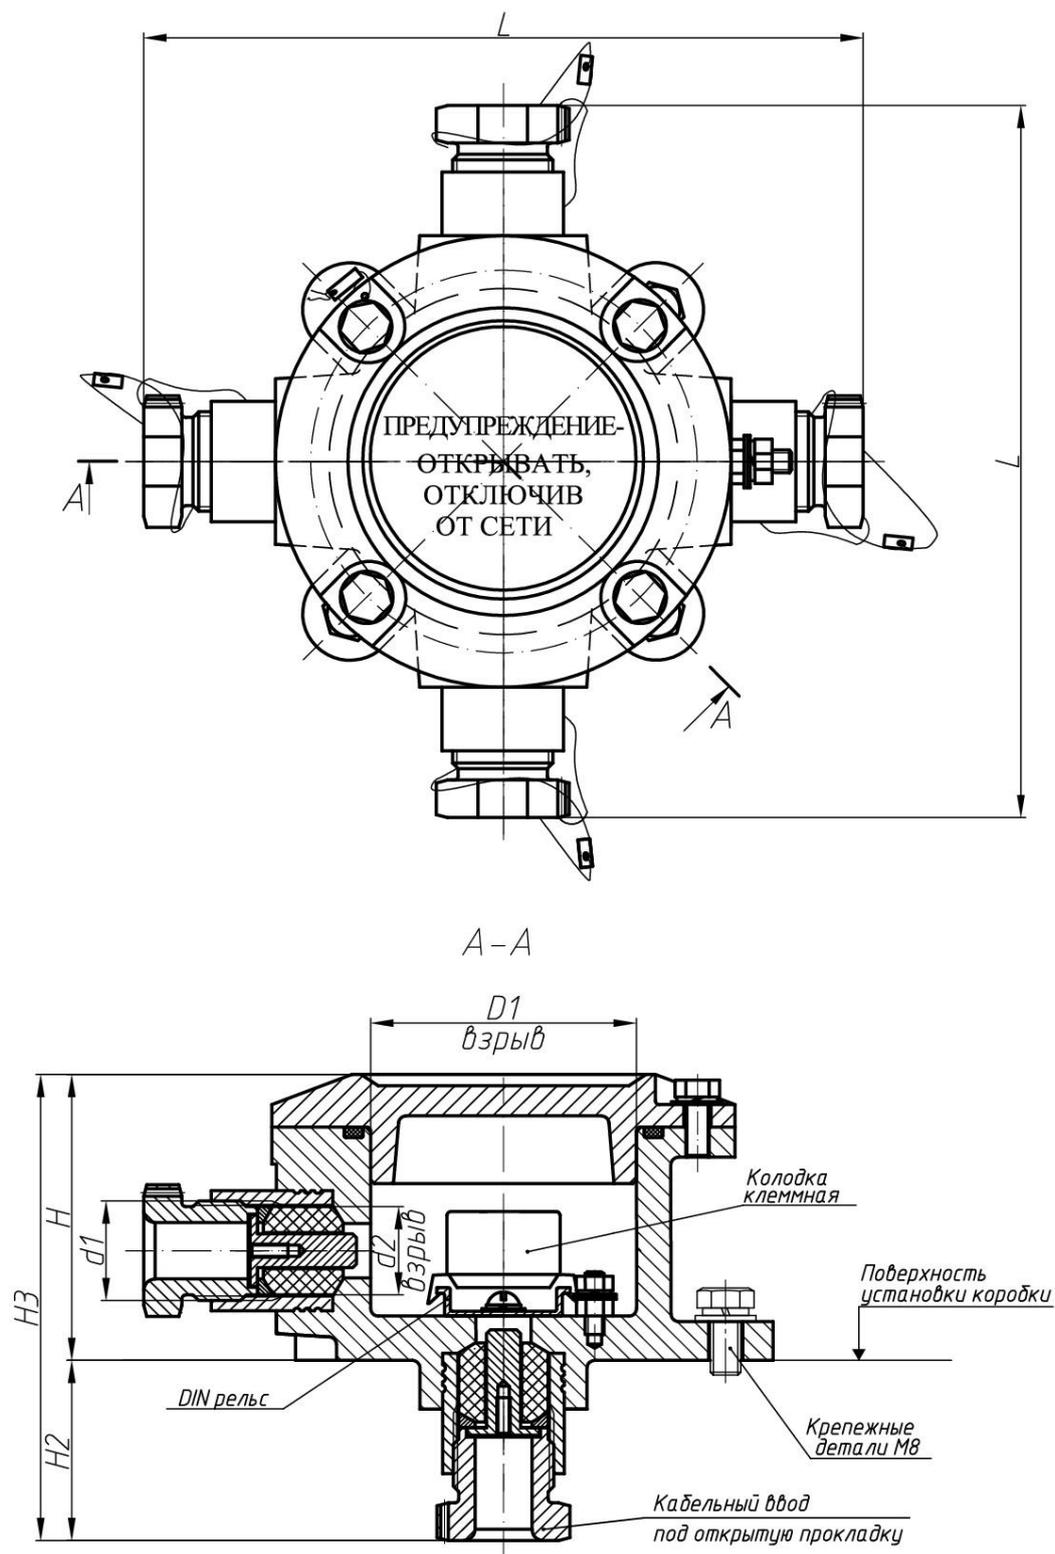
Габаритные, установочные и присоединительные размеры базовой коробки ЕхКСУВ-А
